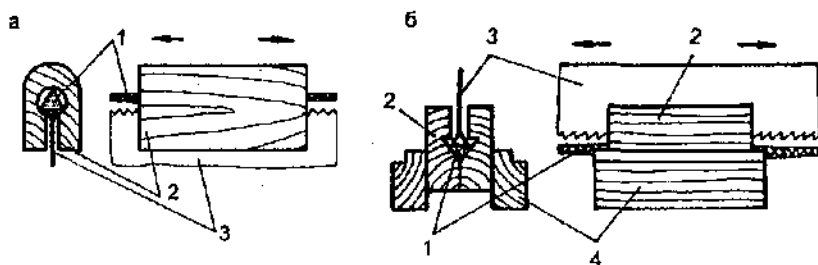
Фугование вершин зубьев пилы: 1 — напильник; 2 — колодка; 3 — пила; 4 — тиски
